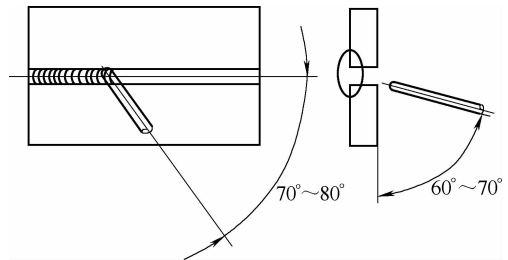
不开坡口对接横焊时的焊条角度
